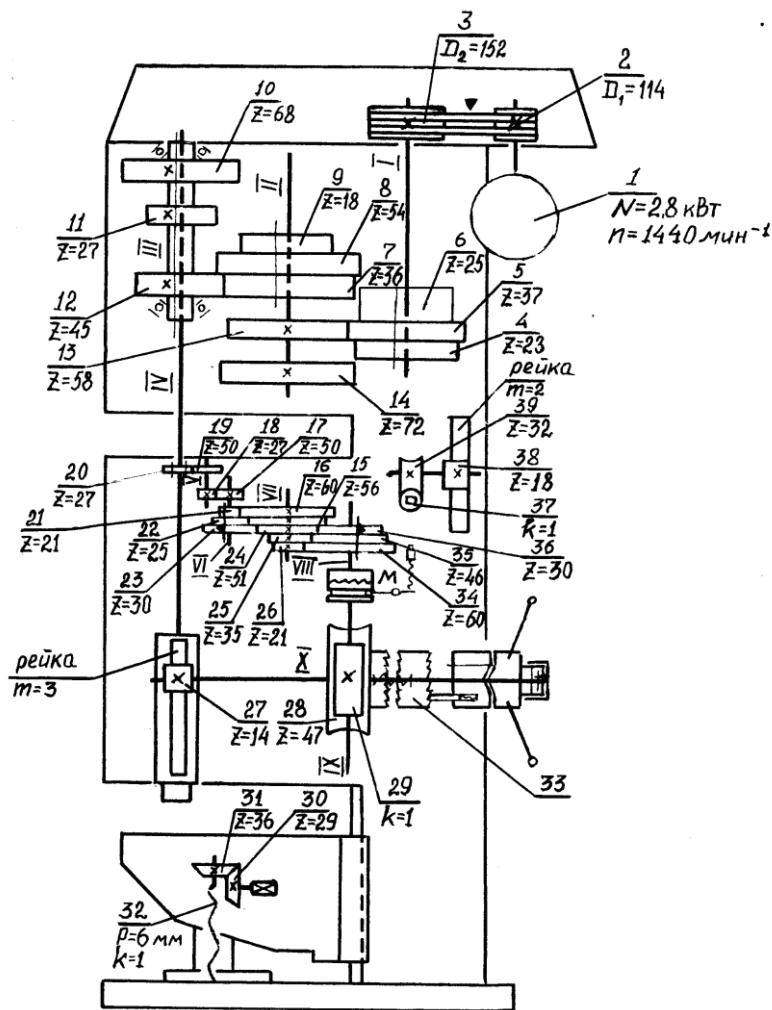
Кинематическая схема вертикально-сверлильного станка 2A125.
